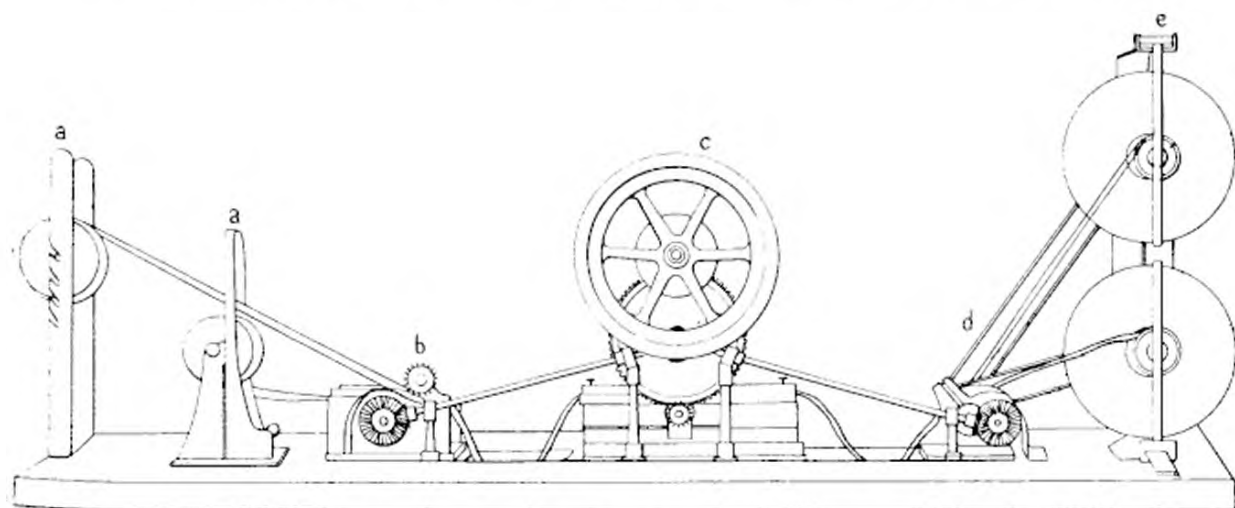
Perforeuse Lux, vue à l'arrière.
